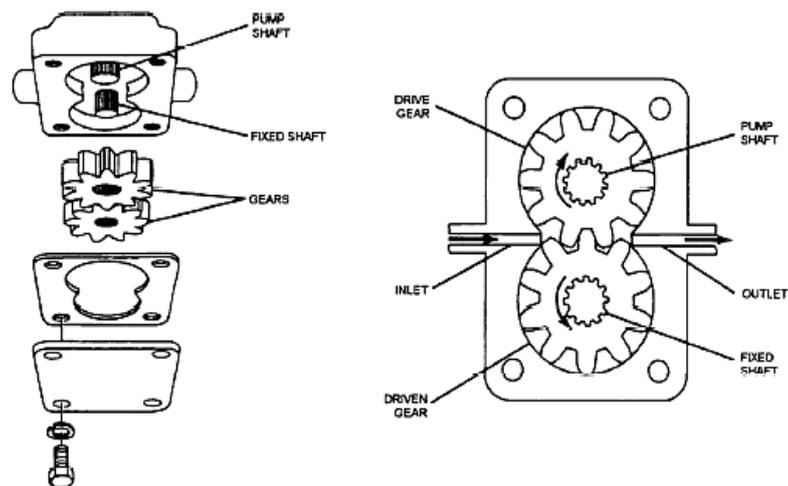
BOMBA DE ENGRANES PARA COMBUSTIBLE
